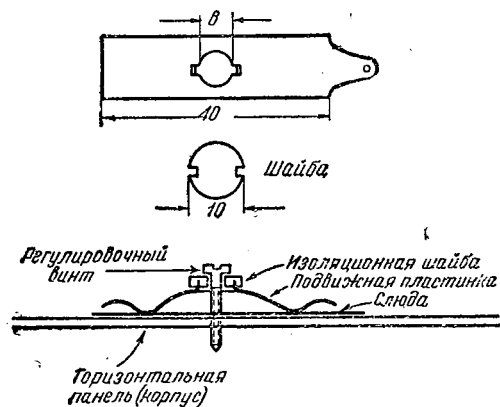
Полупеременный конденсатор и его части (размеры в мм).
